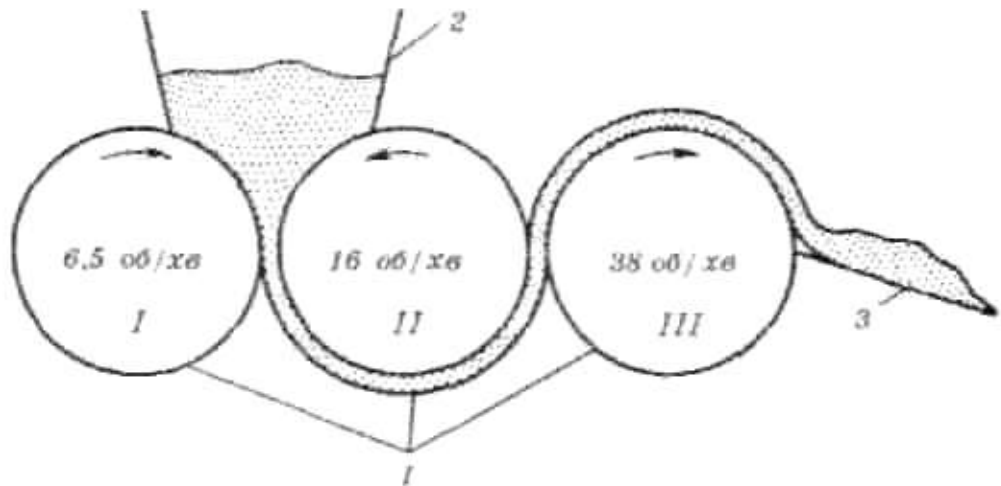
Схема роботи трохвалкового розтирального пристрою
